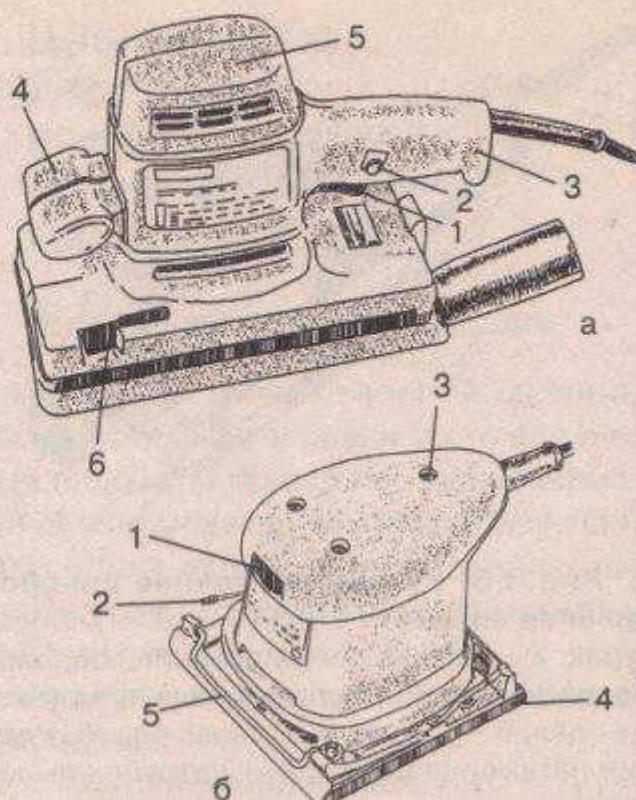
Виброшлифовальные машины: а — крупная: 1 — кнопка-курок; 2 — фиксатор кнопки-курка; 3 — ручка; 4 — вспомогательная рукоятка; 5 — кожух двигателя; 6 — рычаг зажима наждачного полотна; б — малогабаритная: 1 — выключатель; 2 — рычаг; 3 — рукоятка; 4 — платформа из пенорезины; 5 — зажим абразивного полотна
